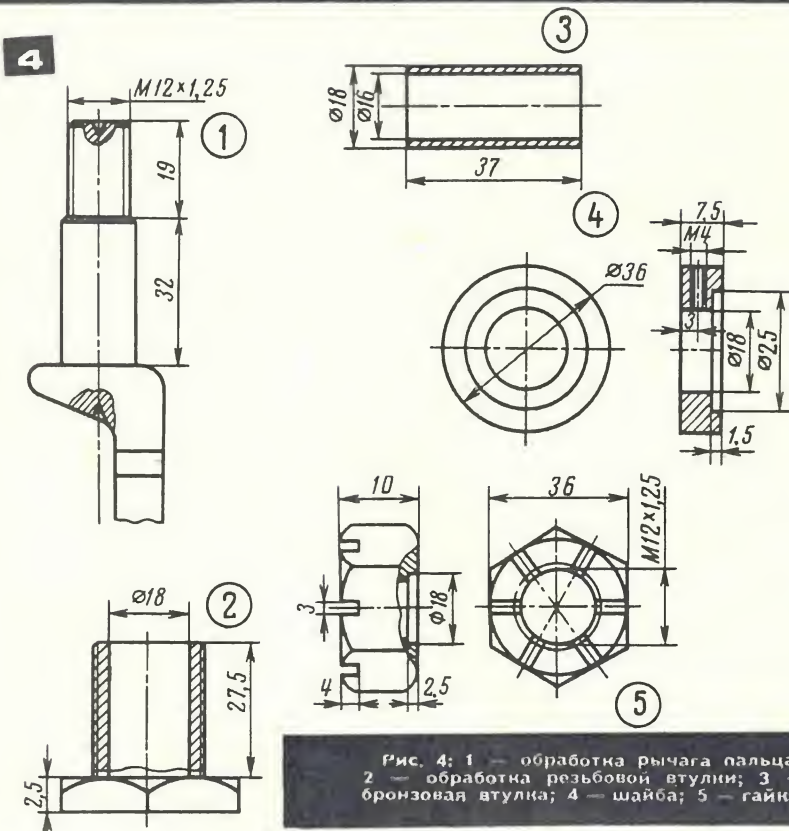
1 — обработка рычага пальца; 2 — обработка резьбовой втулки; 3 — бронзовая втулка; 4 — шайба; 5 — гайка.
